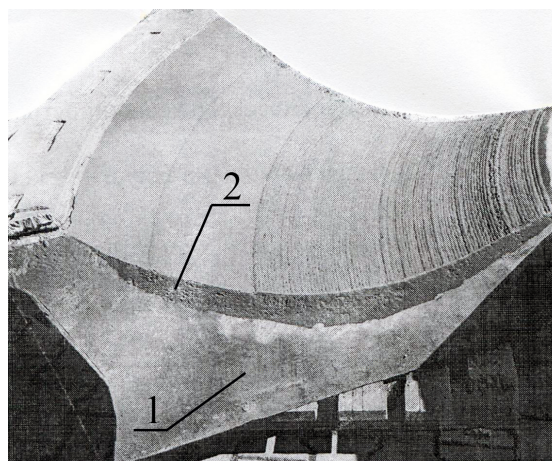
Вид восстановленной рабочей поверхности сегмента помольного стола. 1 — основной металл; 2 — наплавленный слой
